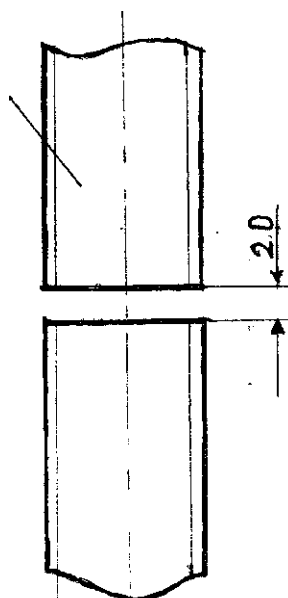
Эскиз сварки труб горизонтальным швом на вертикальной плоскости
